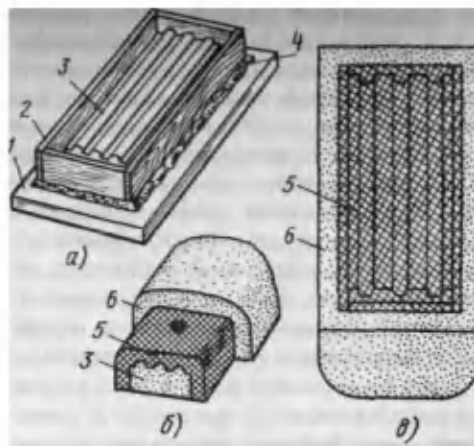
Изготовление клеевой формы открытым способом: а — общий вид форм, б — разрез формы, в — положение формы в кожухе; 1 — плита, 2 — деревянный кожух (бортики), 3 — модель, 4 — стеклянная промазка, 5 — клей, 6 — кожух
